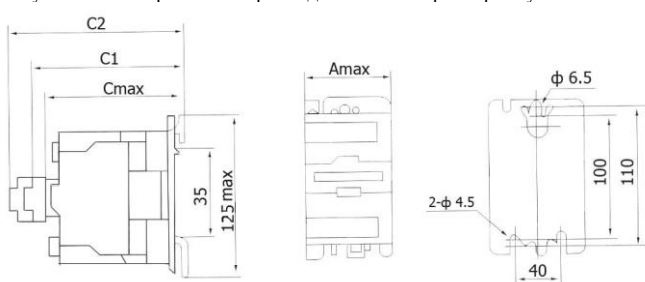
Габаритные и присоединительные размеры пускателей 40-95А
